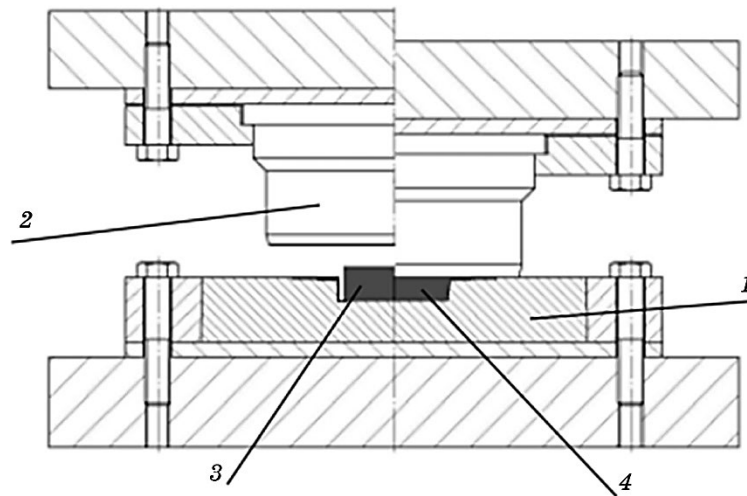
Конструкційна схема штампі для гарячого штампування порошкових заготовок: 1 — матриця, 2 — пуансон, 3 — вихідна заготовка, 4 — поковка.
